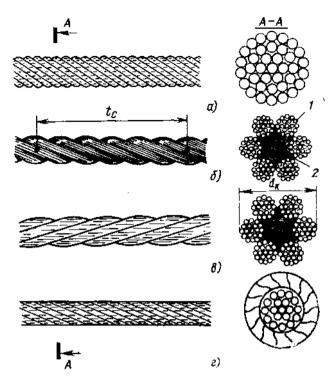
Стальные проволочные канаты: а – одинарной свивки; б – двойной односторонней свивки; в – крестовой свивки; г – закрытый (спиральный); 1 – пряди; 2 – сердечник; t_c – шаг свивки прядей
